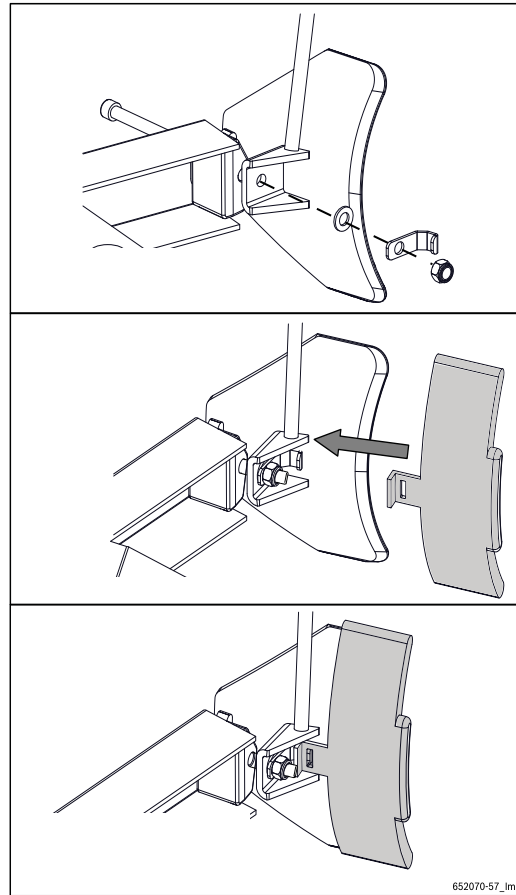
Anbringen des Schutzteils für die Abdrückschaufel
